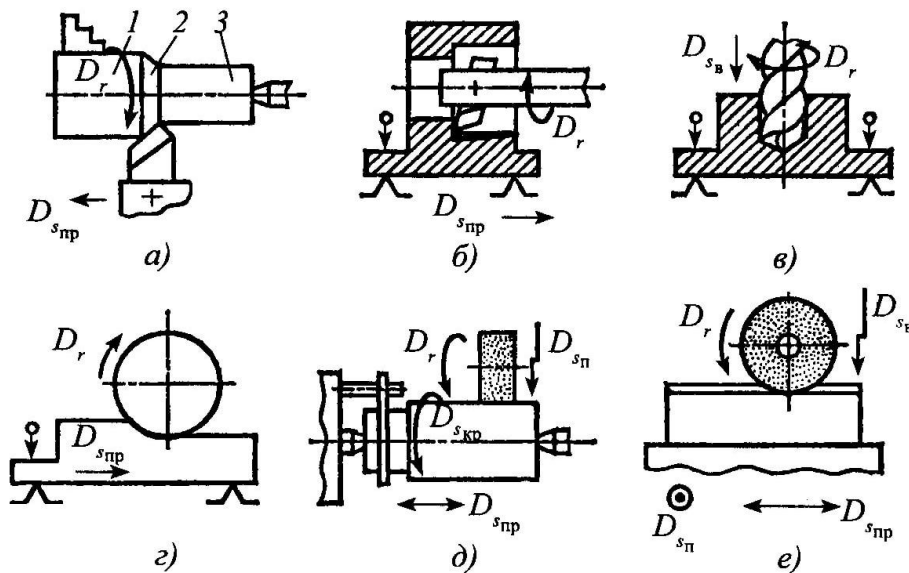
Технологічні способи механічної обробки деталей машин: гострінням (а), розточування (б), свердлінням (в), фрезеруванням (г), шліфуванням на кругло і плоскошліфувальних (відповідно д і е) верстатах
